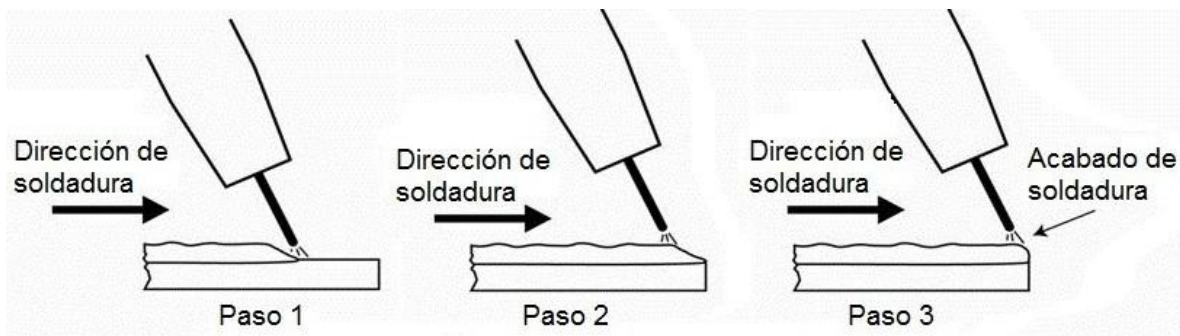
Efecto de la posición del electrodo en el proceso de soldadura MIG-MAG
